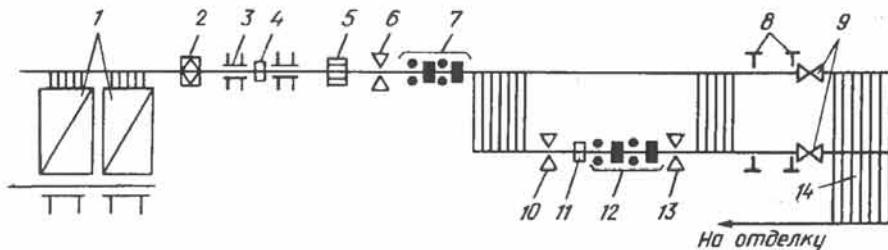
Схема расположения оборудования заготовочного крупносортного стана 700:
